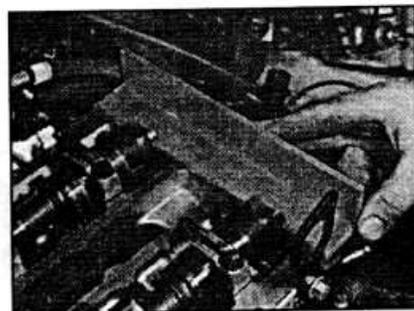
С.12. Установка инструмента Форд 21-162 для фиксации распределительных валов в положении поршней цилиндров №1 и 4 в ВМТ.
